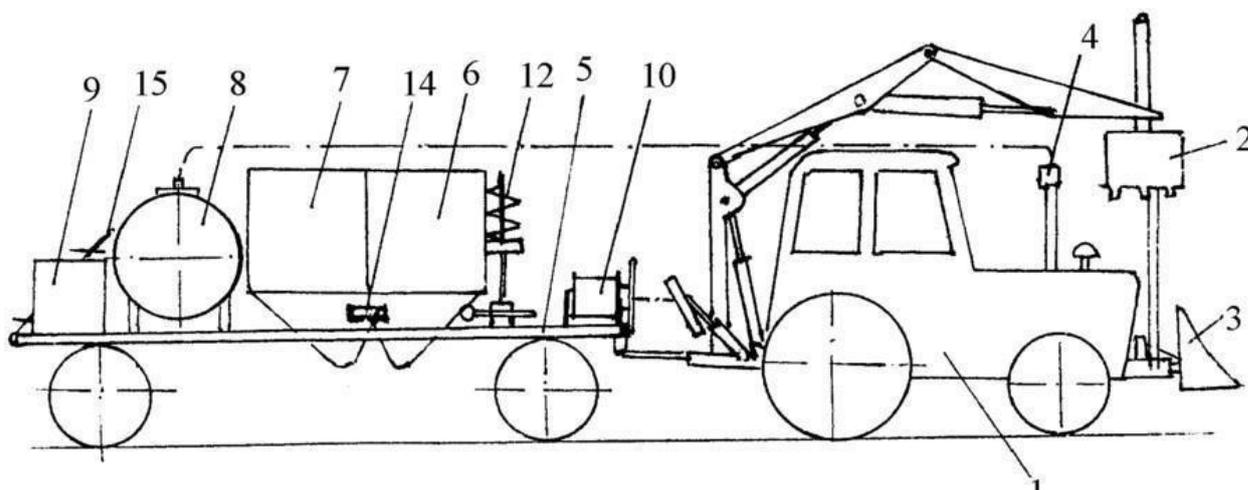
Лесопосадочный агрегат в транспортном положении
